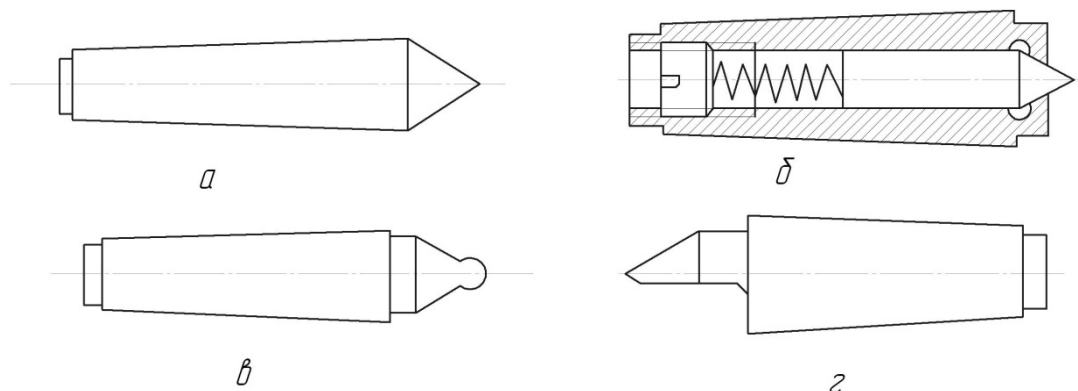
Схемы центров: а – неподвижный (жесткий); б – плавающий (подпружиненный) с опорной торцевой поверхностью корпуса для осевого базирования устанавливаемой в центрах заготовки; в – неподвижный со сферическим наконечником для установки заготовок в центрах с поворотом за счет поперечного перемещения задней бабки; г – полуцентр (срезанный центр), устанавливаемый в пиноль задней бабки для обеспечения обработки торца заготовки со стороны центрового гнезда
